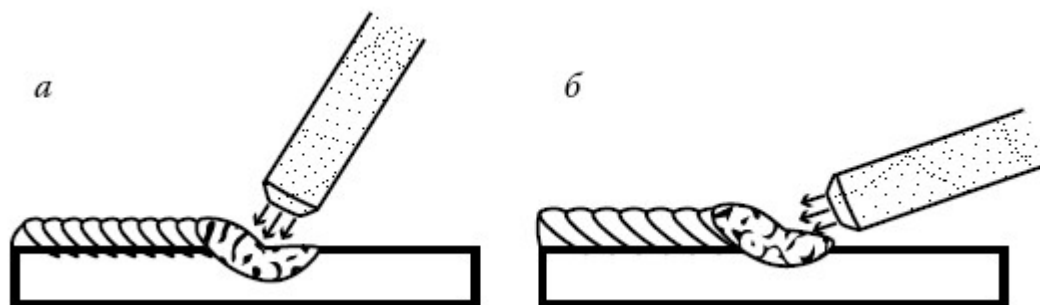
Манипулирование сварочной ванной с помощью силы дуги:
